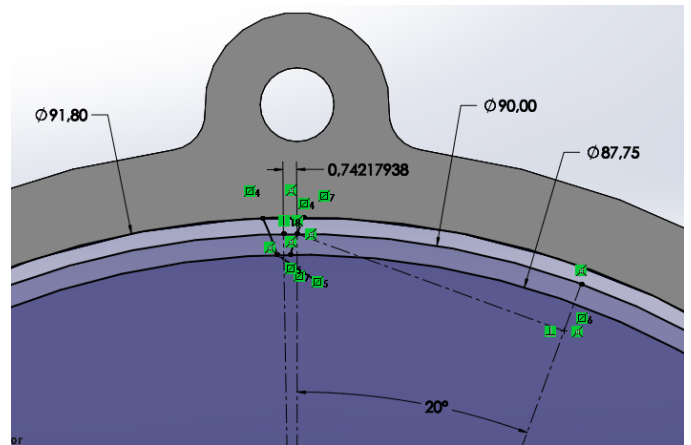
Croquis de diseño de engrane externo de 100 dientes.
